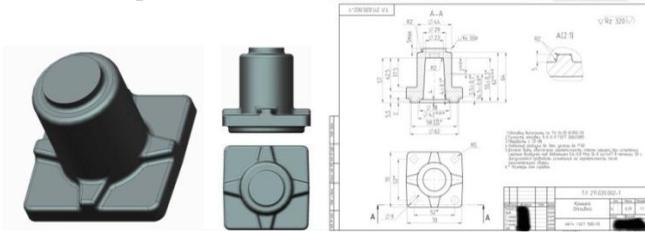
Изображение ЭМИ и чертежа детали «крышка отливка ТЛ 211.020.002-1»
